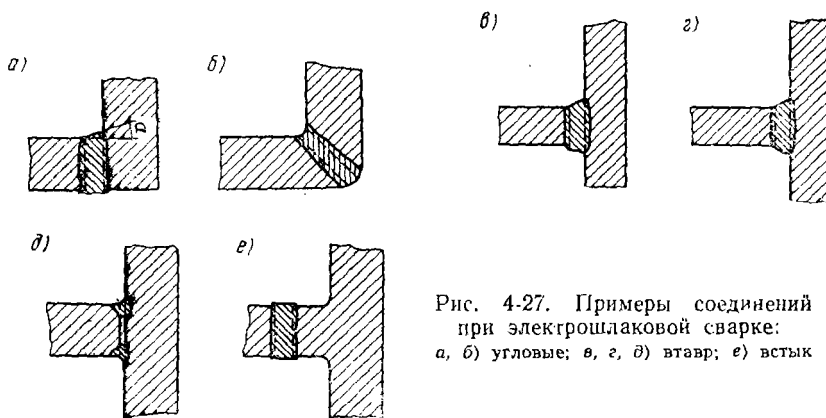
Примеры соединений при электрошлаковой сварке: а, б) угловые; в, г, д) втавр; е) стык
